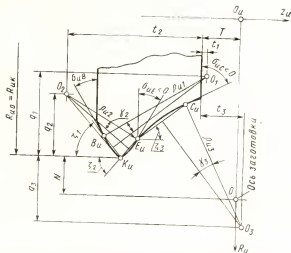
Схема замены дугами окружностей теоретического профиля дисковой фрезы для обработки канавок под винтовые пластинки из твердых сплавов
